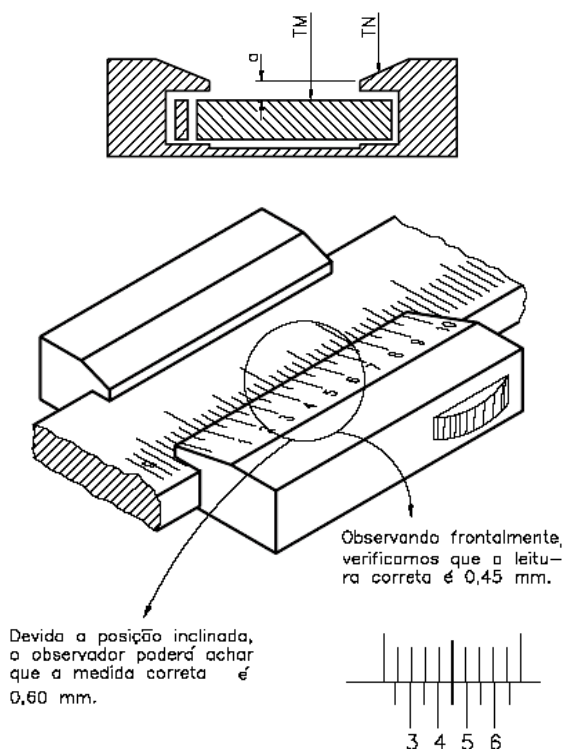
Representação esquemática de parte de um paquímetro em corte com vista frontal e detalhe tridimensional.
